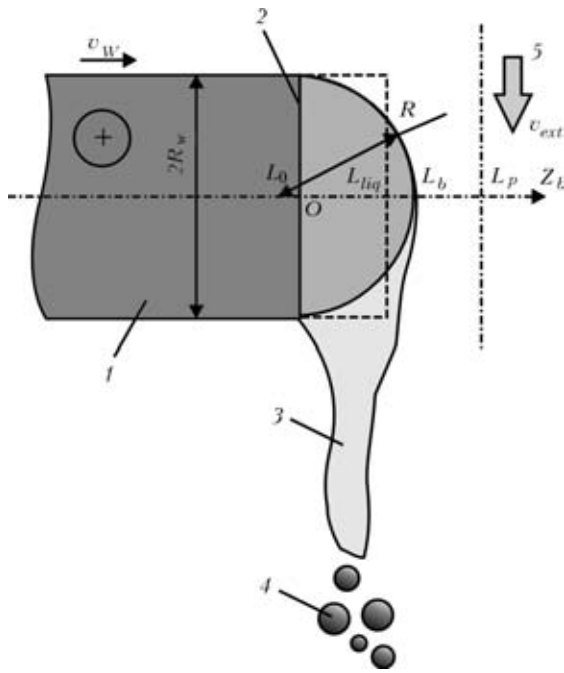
Схема формирования жидкой прослойки на торце токоведущей проволоки при плазменно-дуговом напылении: 1 — токоведущая проволока; 2 — граница плавления; 3 — струя расплавленного металла («язык»); 4 — напыляемые частицы; 5 — плазменный поток
